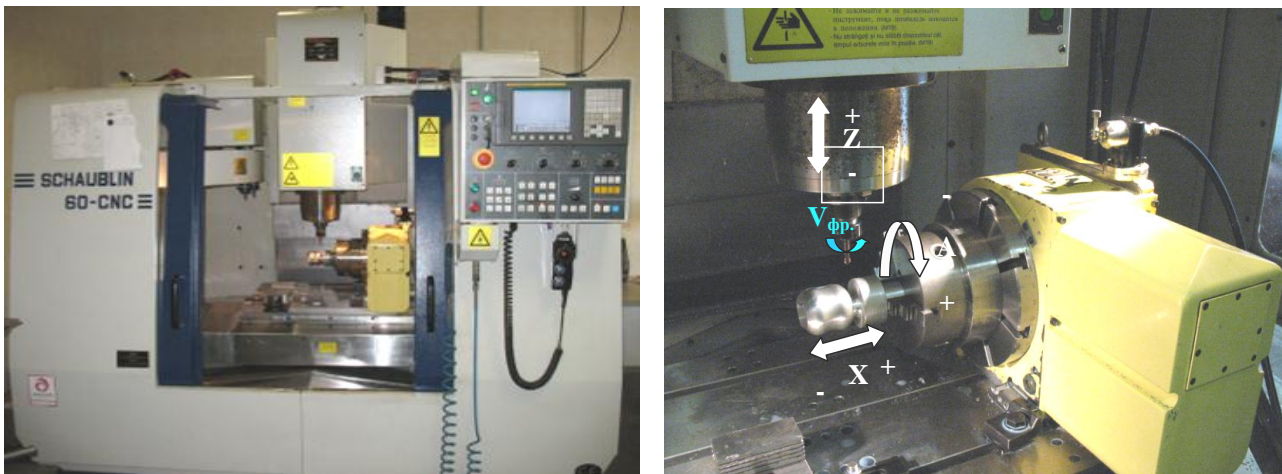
Умови проведення експерименту: а) загальний вигляд верстату; б) - схема формоутворення робочої поверхні ендопротеза
